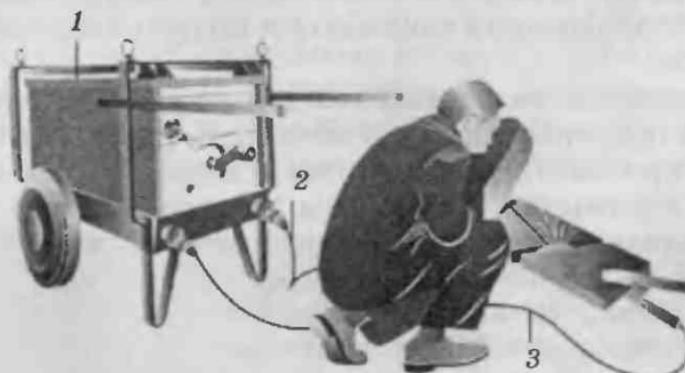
Схема поста для ручной дуговой сварки:
